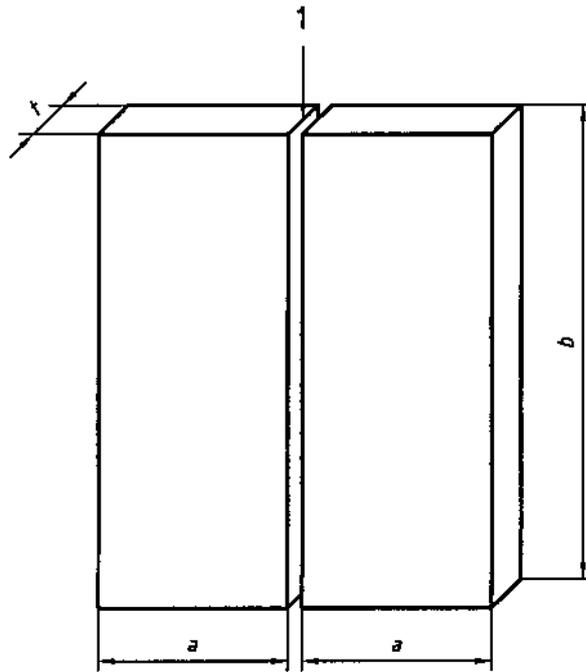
Образец для испытаний стыкового соединения пластин с полным проплавлением при сварке
